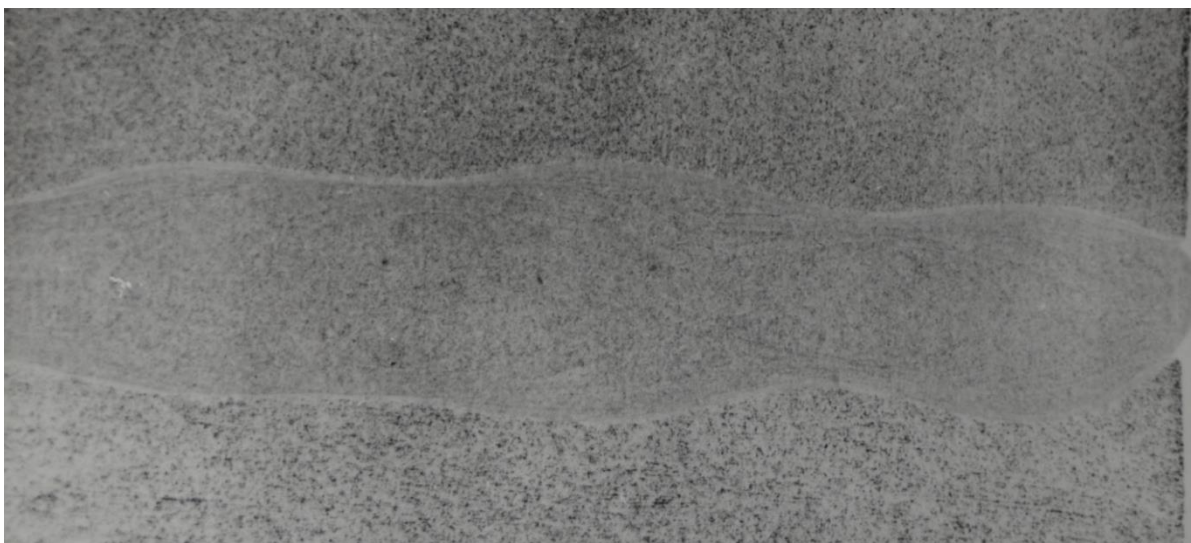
Серный отпечаток по Бауману поперечного сечения сварного соединения
